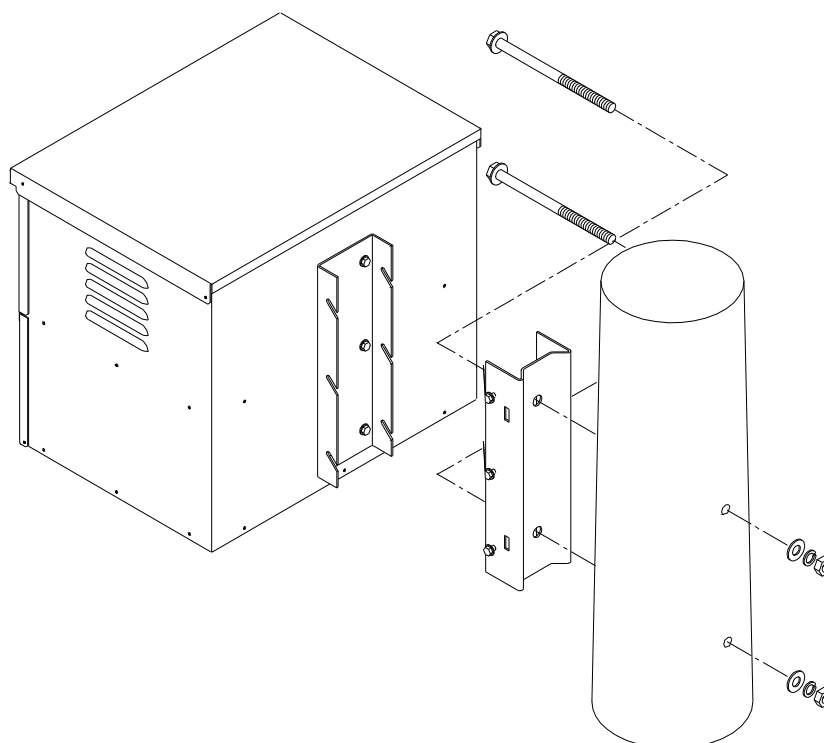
Instalação do Gabinete Externo em Poste de Madeira
